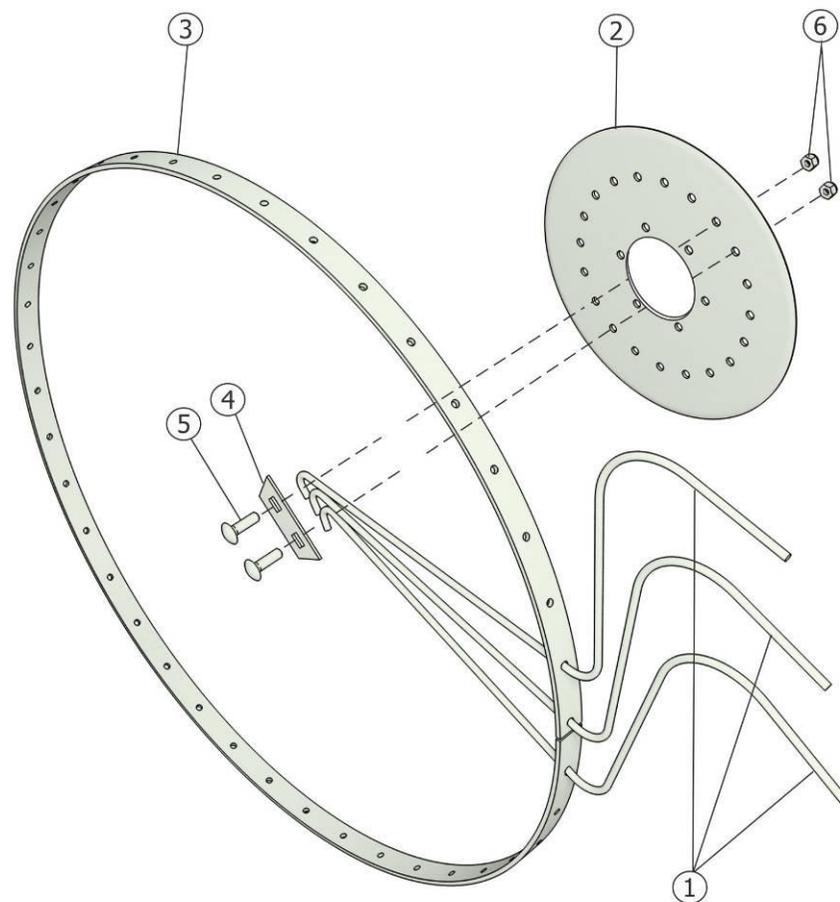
Колесо рабочее ГКП -601.00.050-02. Колесо рабочее ГКП -601.00.050-03
